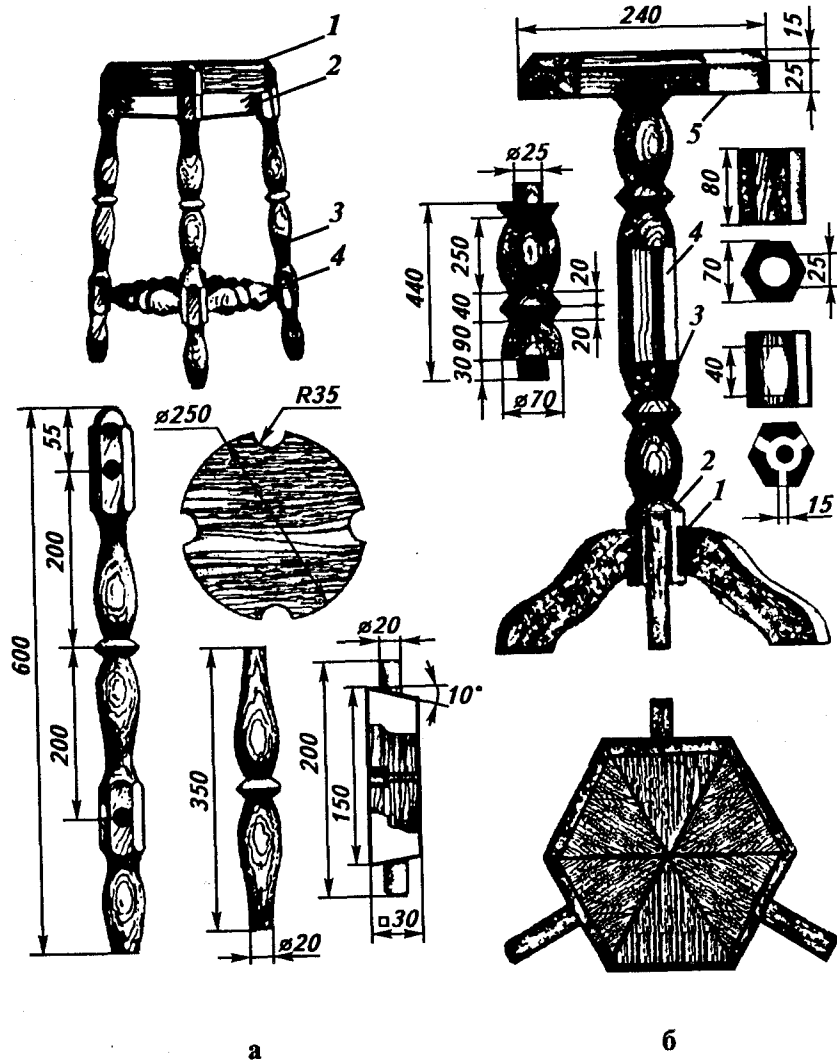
Изделия с точеными деталями: а – стул: 1 – крышка; 2 – царга; 3 – ножка; 4 – проножка; б – стол: 1 – ножка; 2, 3, 4 – детали стойки; 5 – крышка
